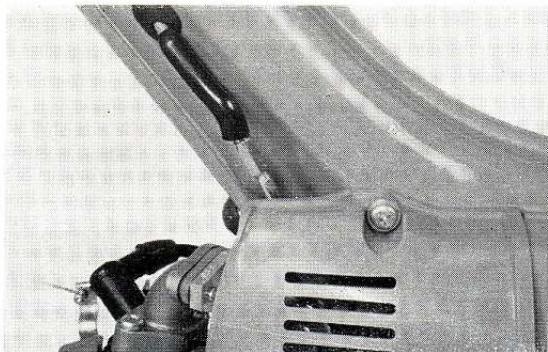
REGLAGE DU CABLE D'ETRANGLEMENT.
